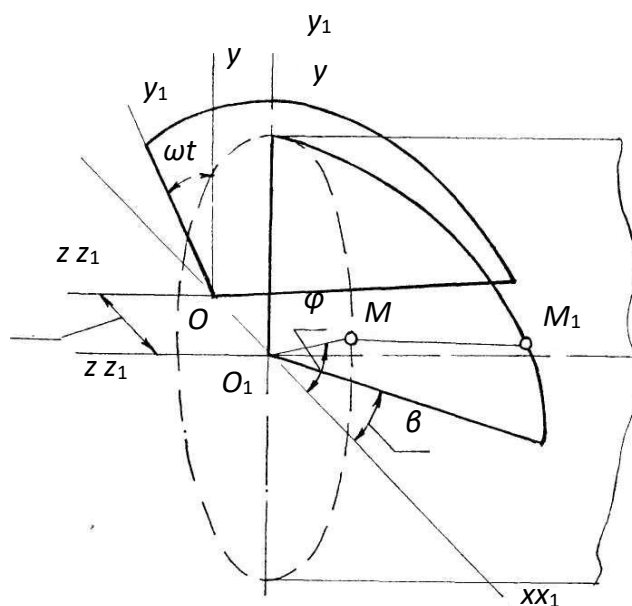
Схема движения точек фрезерных ножей зубцеобразной формы
